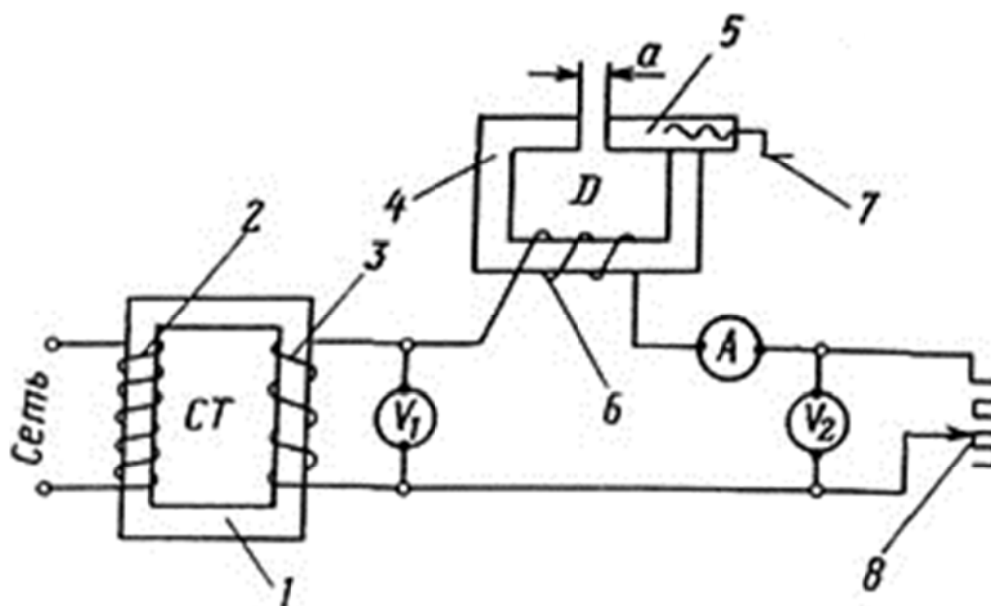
Схема сварочного трансформатора с отдельным дросселем:
